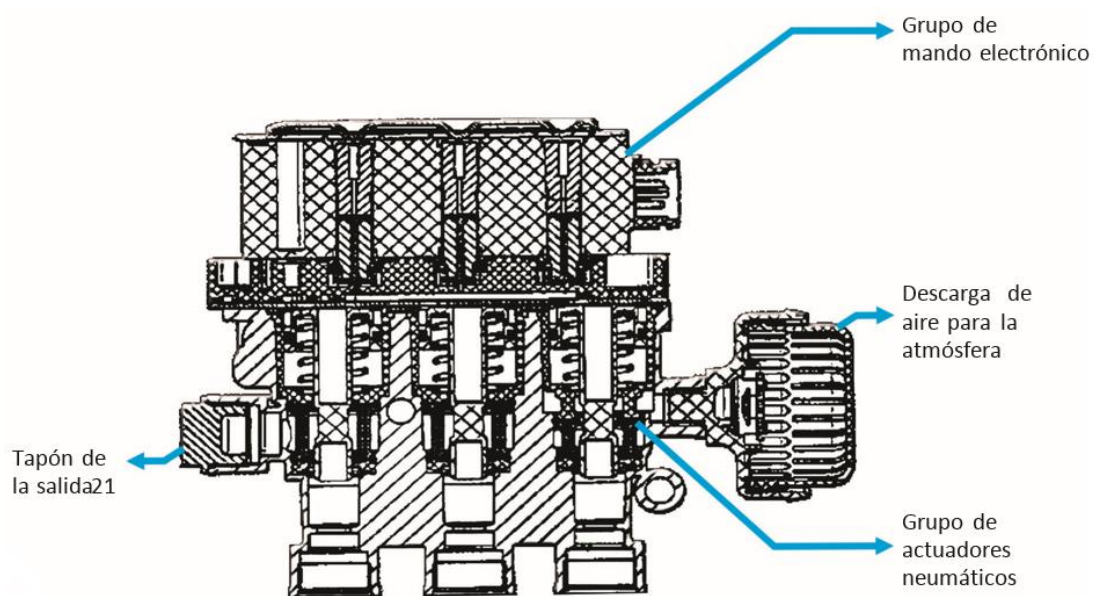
Detalles constructivos conjunto válvula solenoide/sistema neumático.
